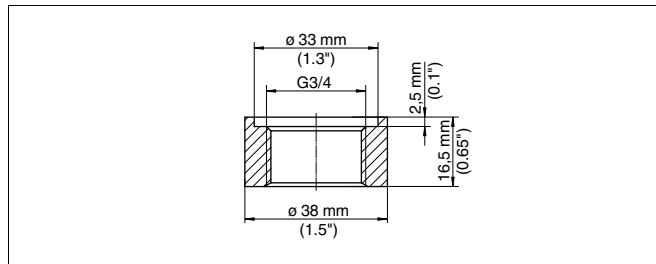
Maße Einschweißstutzen G $\frac{3}{4}$  A nach DIN 3852-X
